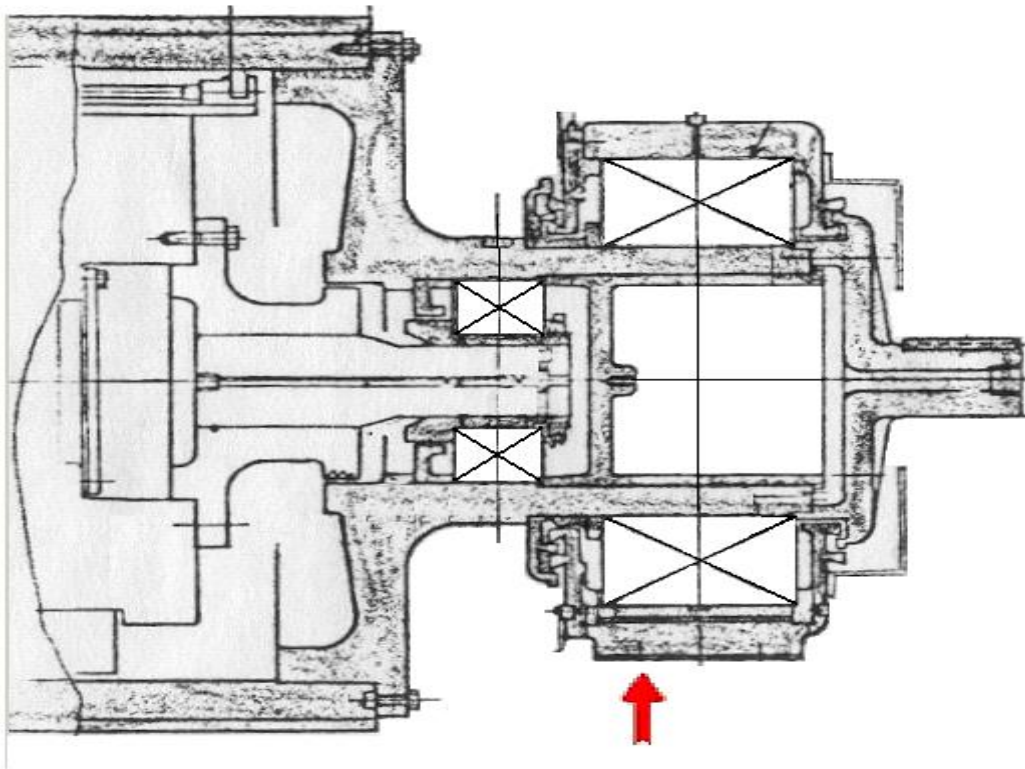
Схематичное представление исследуемого узла (подшипники отсасывающего вала)
